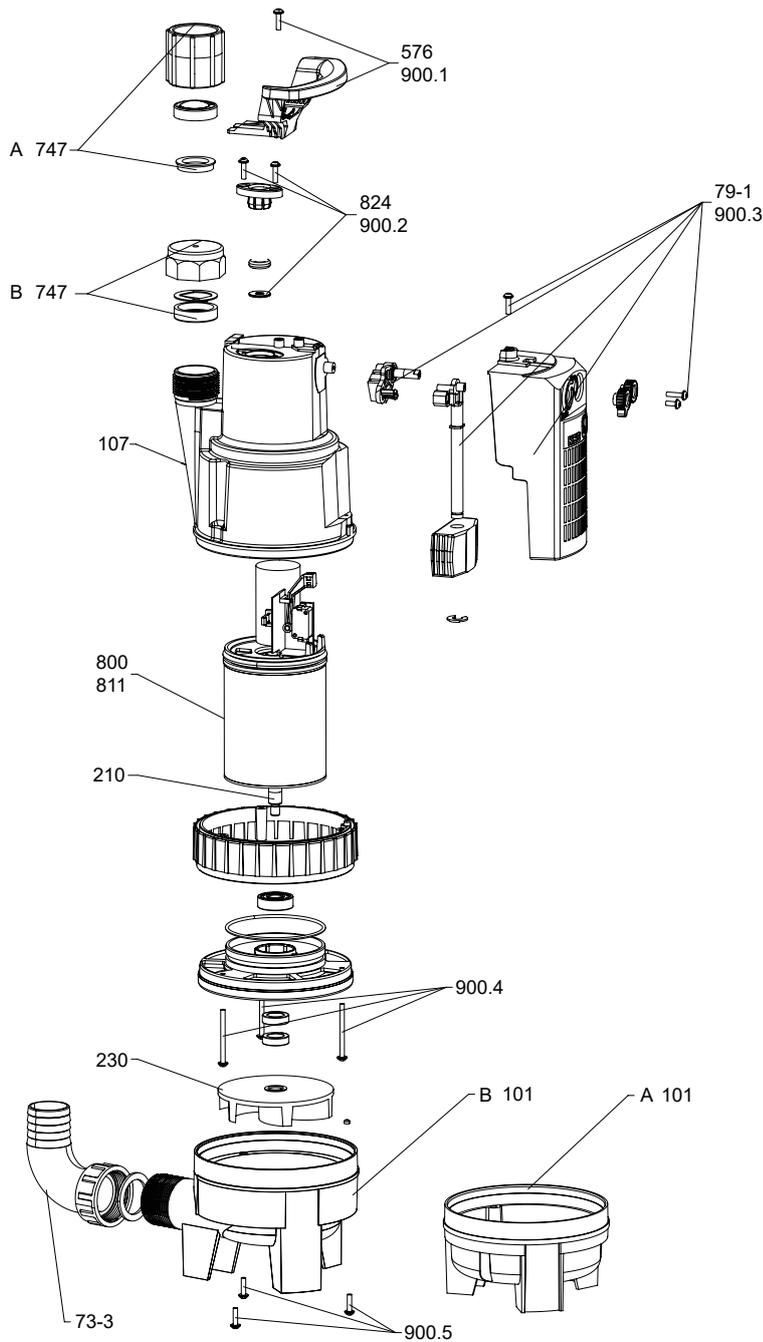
Explosionszeichnung AmaDrainer 322, 354
